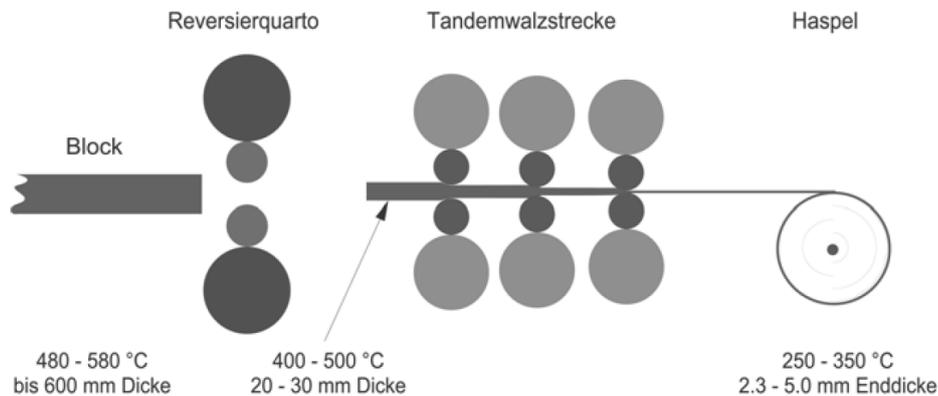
Warmwalzstrecke für ein Bandwalzwerk<sup>367</sup>
